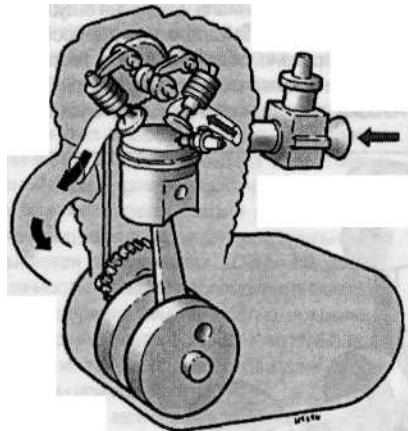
б Типичный одноцилиндровый четырехтактный двигатель
